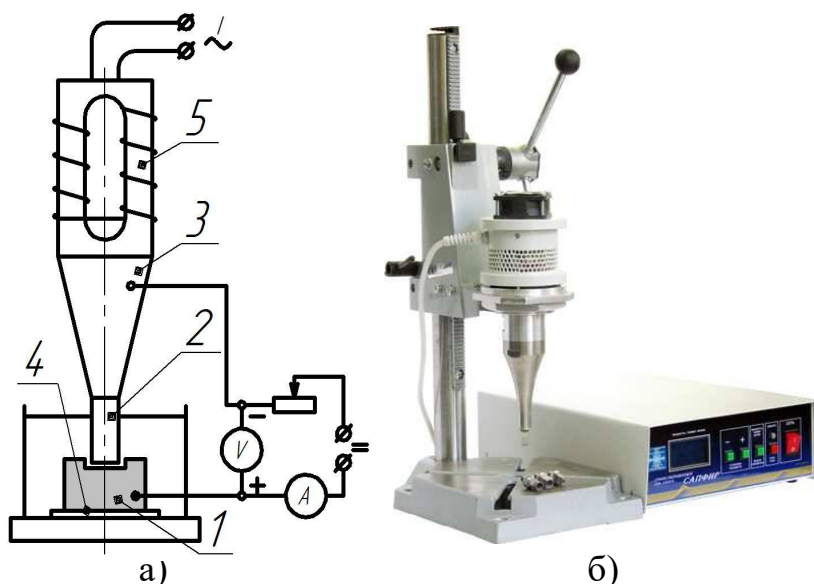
Схема ультразвукової обробки (а) та ультразвуковий верстат (б): 1 – заготовка; 2 – інструмент; 3 – акустичний концентратор; 4 – прокладка; 5 – соленоїд
